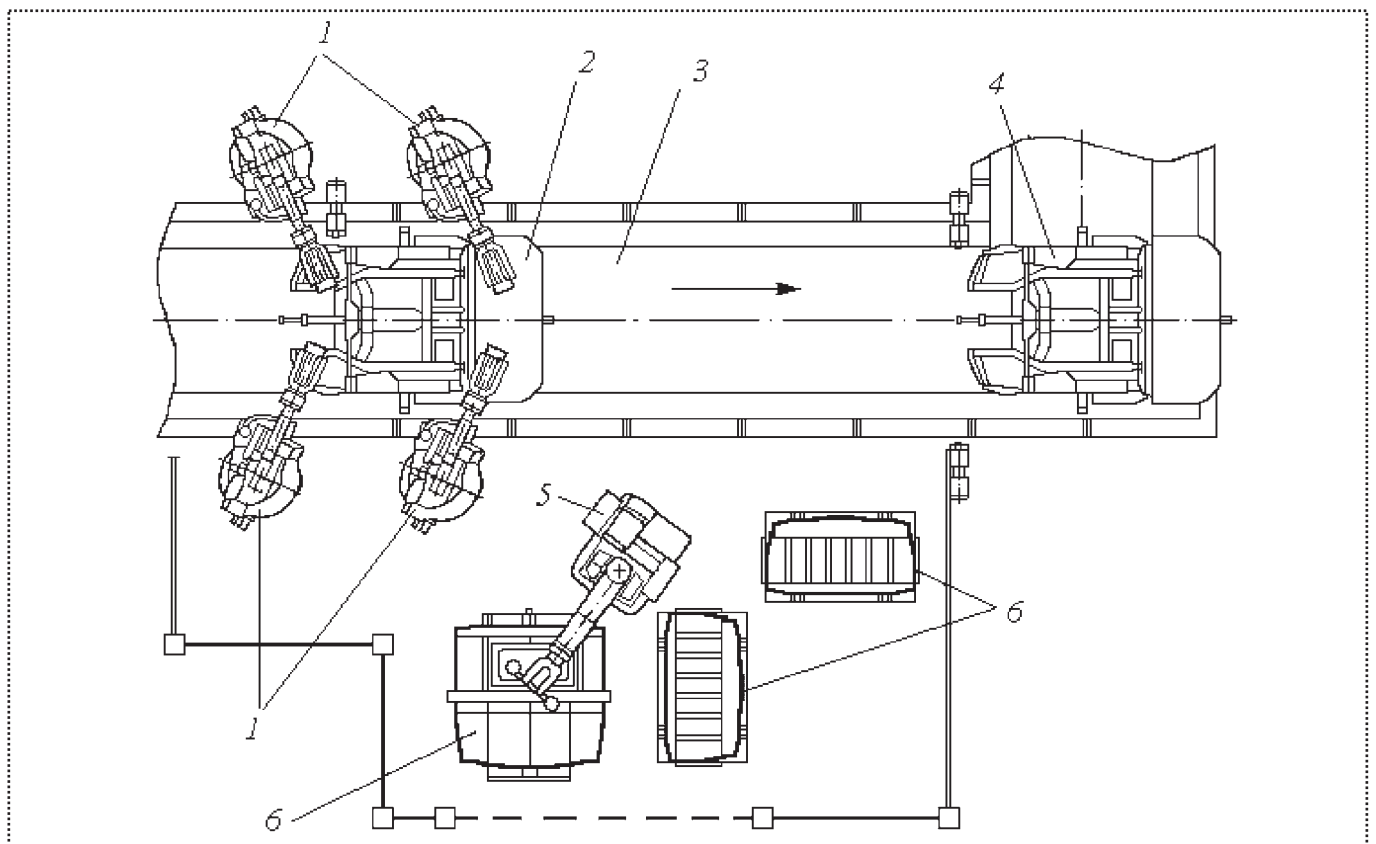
Роботизированный участок приварки крыши к основанию кабины грузовых автомобилей семейства "Газель" в составе линии сборки-сварки кабин
